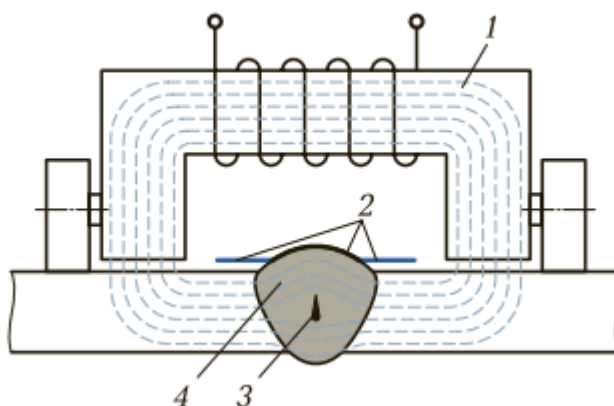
Схема магнитографического контроля: 1 — намагничивающее устройство; 2 — магнитная пленка; 3 — дефект; 4 — сварной шов
